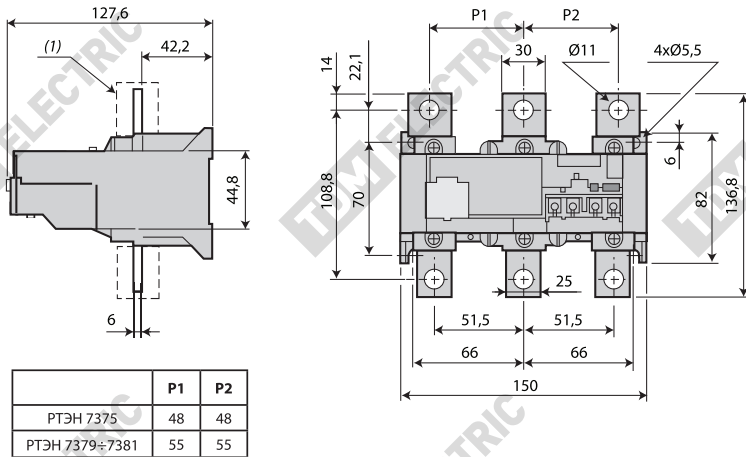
Габаритные и установочные размеры PTЭН-7375÷7381, мм
